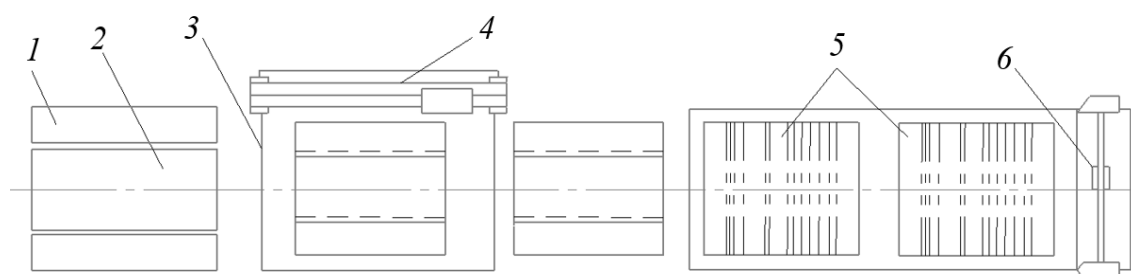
Схема поточной линии сборки и сварки секций крыши
